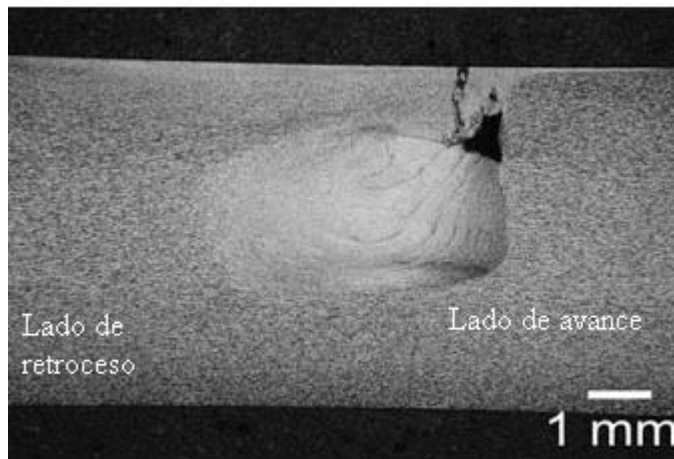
Micrografía mostrando un hueco, defecto en soldadura FSW, Leonard et al. (2003).
